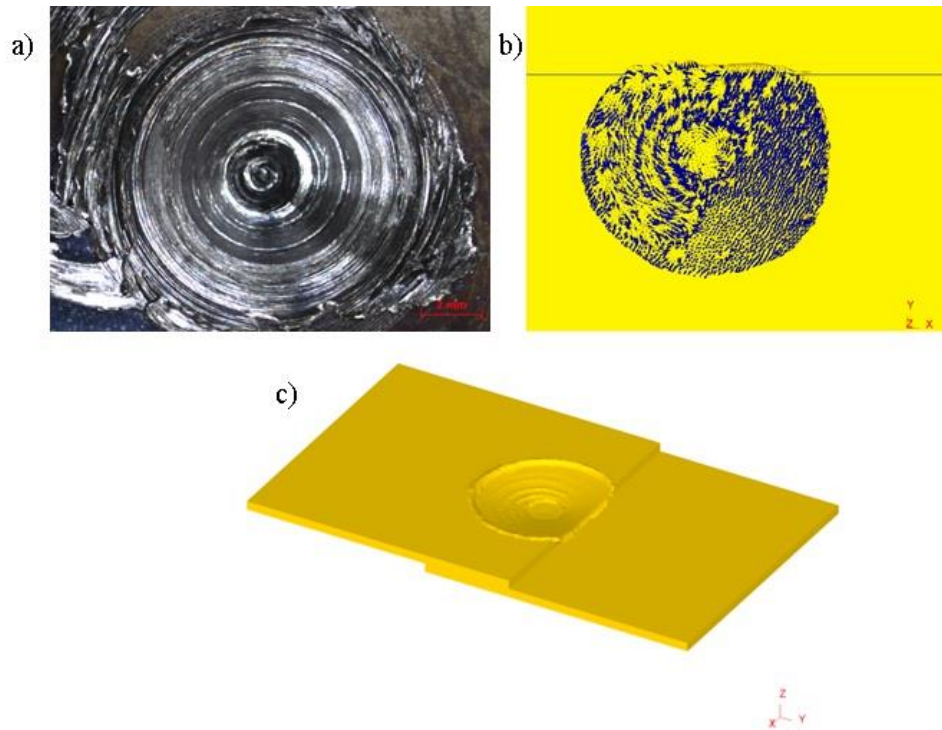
Flujo del material en el punto de soldadura mediante el proceso de soldadura FSSW, a) Imagen del punto de soldadura generado mediante el proceso FSSW, b) representación del flujo del material en la unión por MEF y c) huella de la herramienta mediante MEF.
